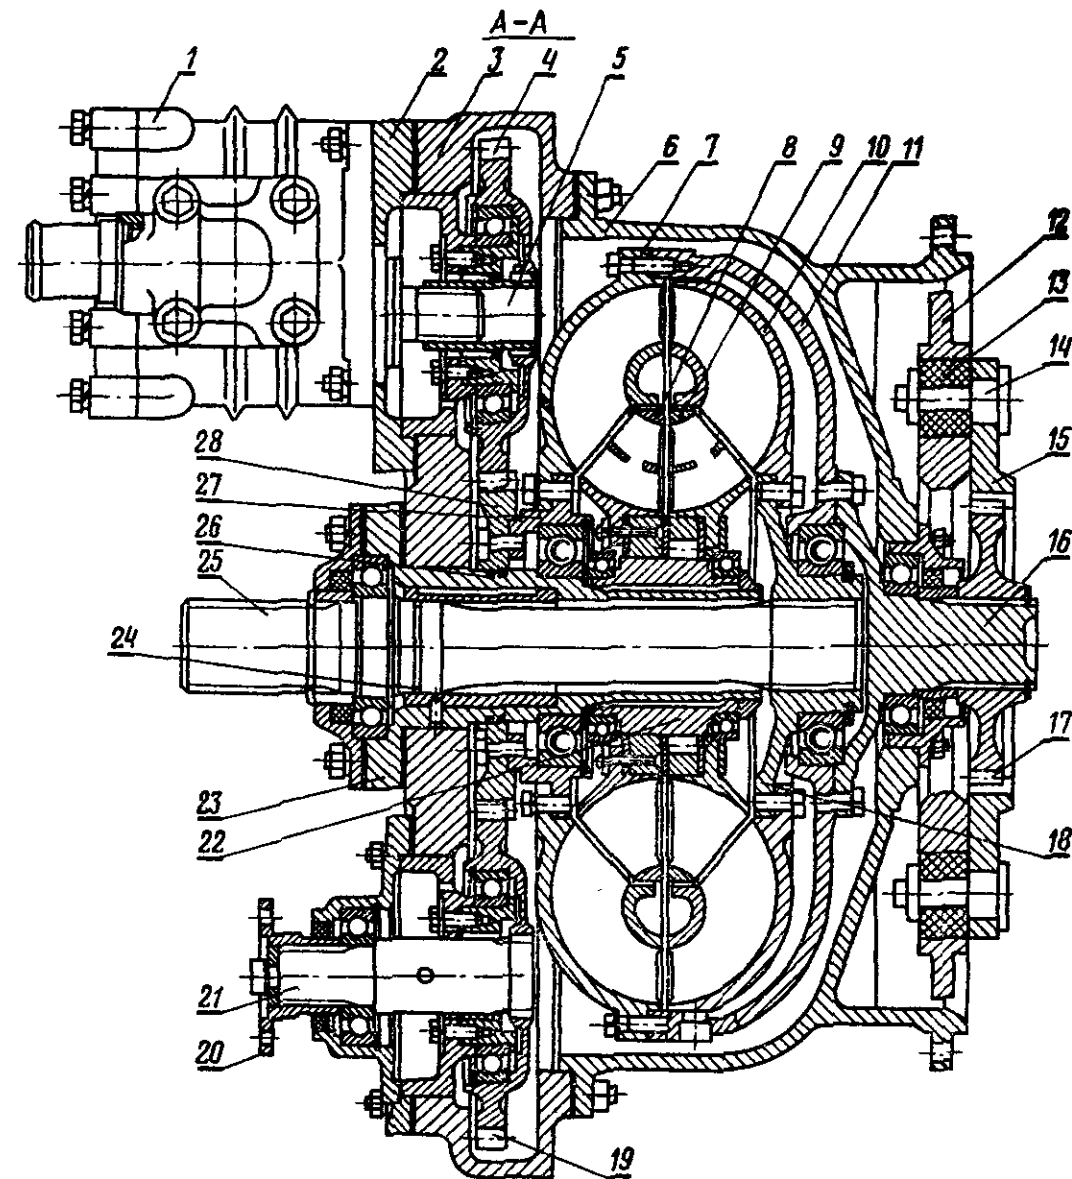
Гидротрансформатор трактора К-702 (продольный разрез): 1 и 31 — гидронасосы; 2 и 27 — стаканы; 3 — проставка; 4, 19 и 28 — шестерни; 5 — компенсирующее устройство; 6 — корпус; 7, 8, 9 и 10 — колеса; 11 — барабан; 12 — ведущий диск; 13 — амортизатор; 14 — палец; 15 — ведомый диск; 16, 18 и 23 — ступицы; 17 — зубчатая муфта; 20 — фланец; 21 и 25 — валы; 22 — втулка; 24 и 26 — уплотнительные чугунные кольца; 29 — клапан подпитки; 30 — регулятор расхода.
